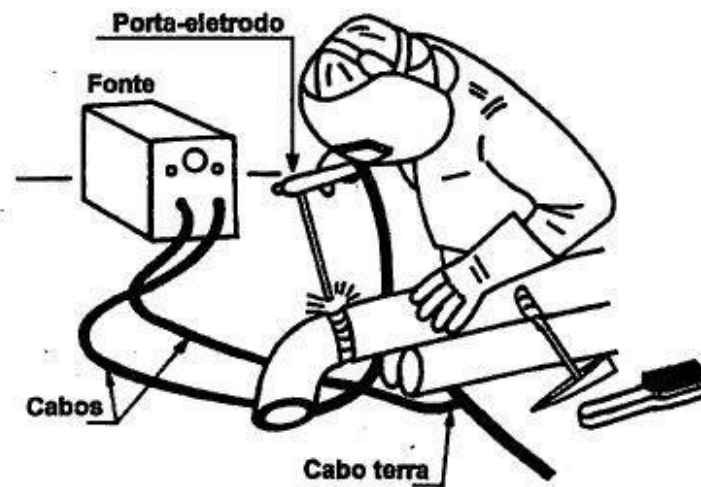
Equipamentos de soldagem SMAW (Adaptado de [20]).
